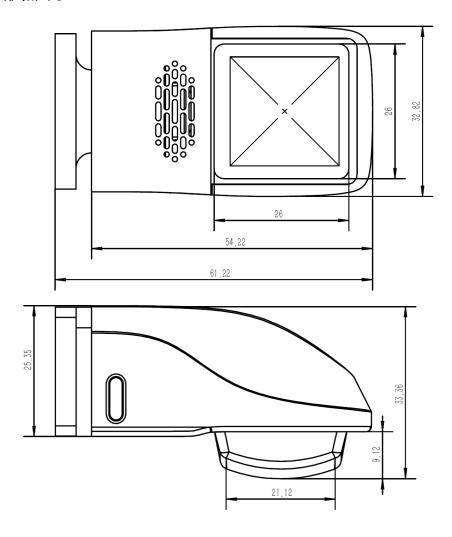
Tac3D-AD2 触觉传感器外形尺寸
